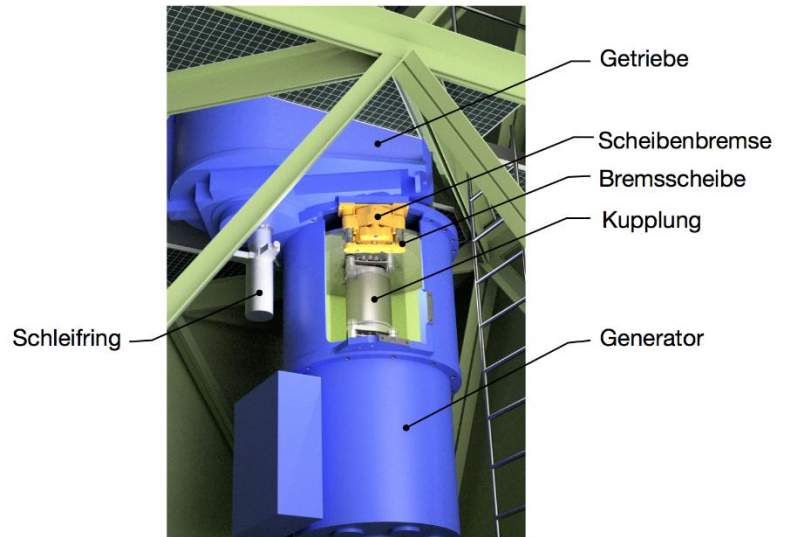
Ausschnitt Maschinenhaus, Rotorbremse
